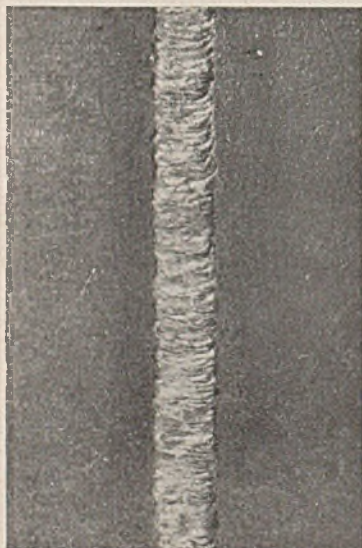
Senkrecht verlaufende Schweißnaht mit einer Arcos-Carend-Elektrode der Arcos Gesellschaft für Schweißtechnik.
